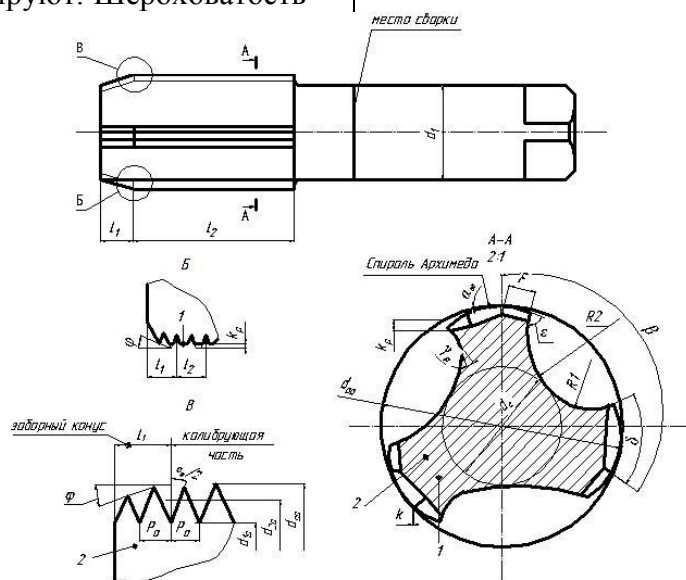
Конструкция комбинированного режущего-деформирующего чистового метчика: 1 – режущий зуб; 2 – деформирующий выступ
